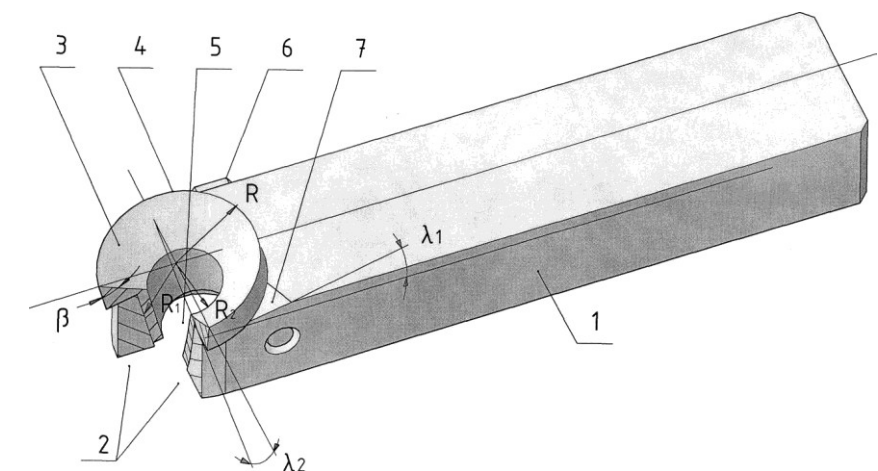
Резец с радиусной режущей кромкой: 1 – стальной корпус резца; 2 – головка; 3 – хвостовик режущего элемента; 4 – торцевая режущая кромкой радиусом R ; 5 – сквозное отверстие радиусом R_2 для удаления стружки; 6 – стопорный болт; 7 – отверстие радиусом R_1 в головке резца перпендикулярно плоскости, которая наклонена вдоль корпуса резца под углом λ_1 относительно горизонтальной плоскости и одновременно под углом λ_2 в вертикальной плоскости
